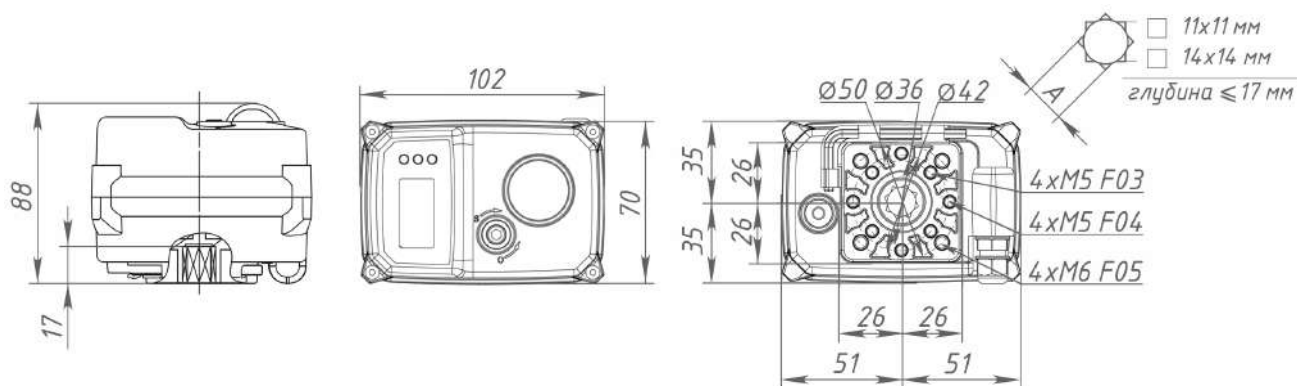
Габаритные размеры электроприводов Motorvalve серии Basic B20.
